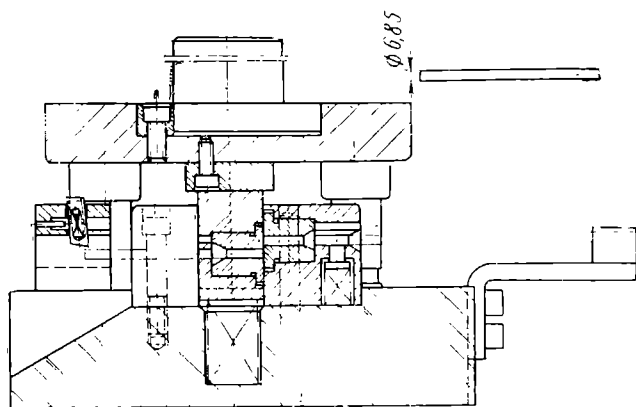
Штмп (а) для рубки заготовок (б) из прутка
